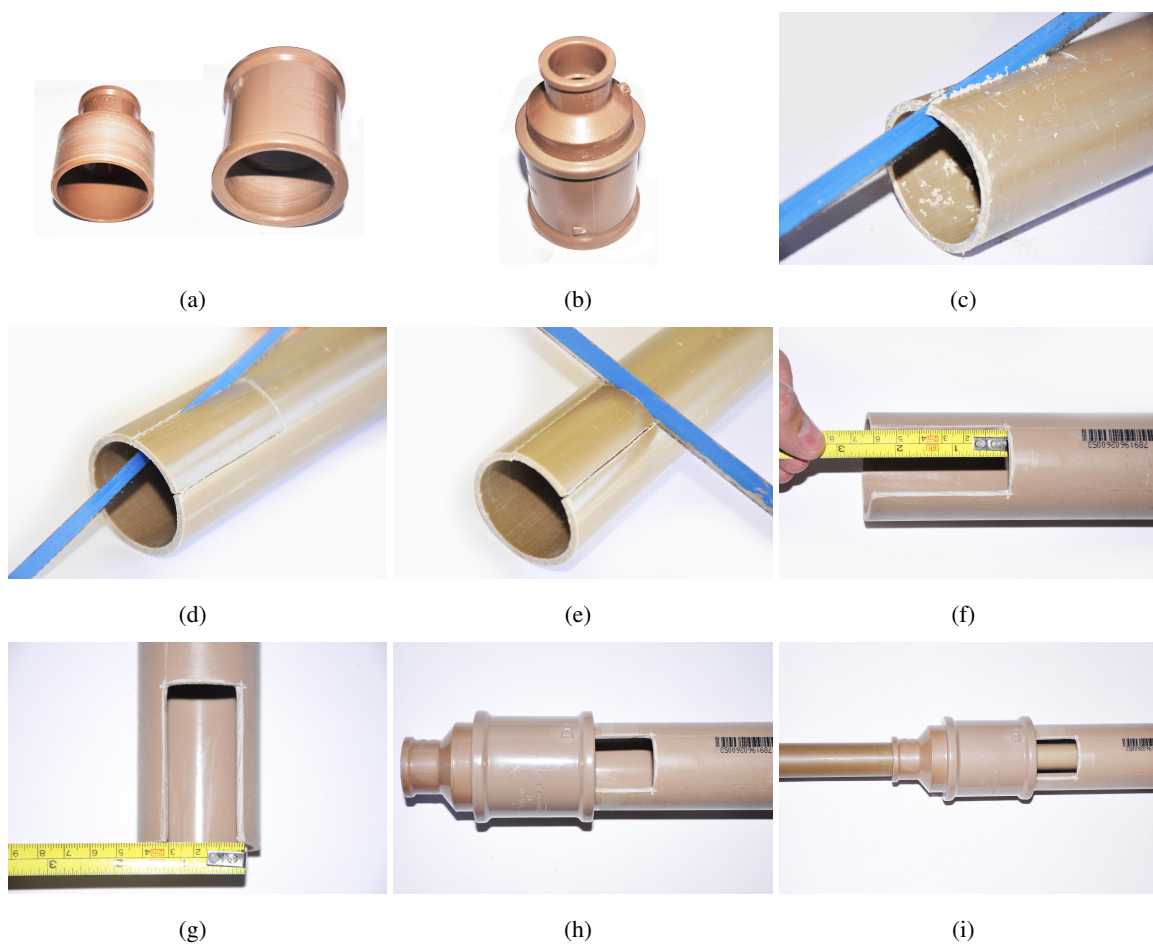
Sequência de montagem da parte superior do corpo da bomba.
